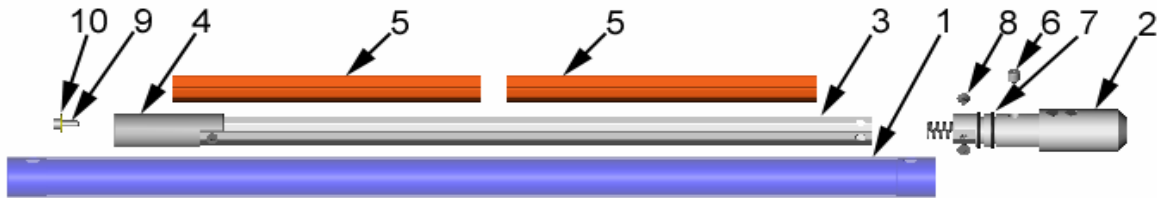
Outil de coupe Split Shot Cutter avec plateau - Vue éclatée
